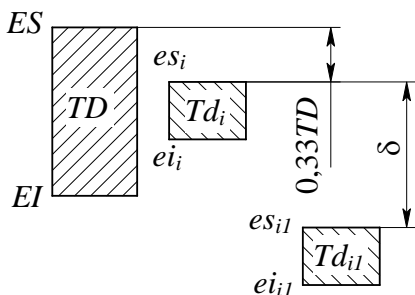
Схема відносного положення допуску розвертки і деталі
